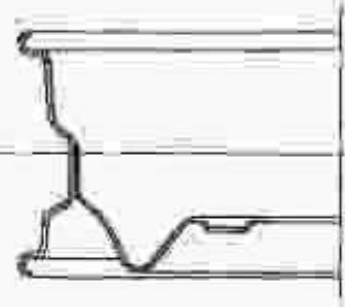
Joints à bords plats et arrondis (1er et 2e montages).
